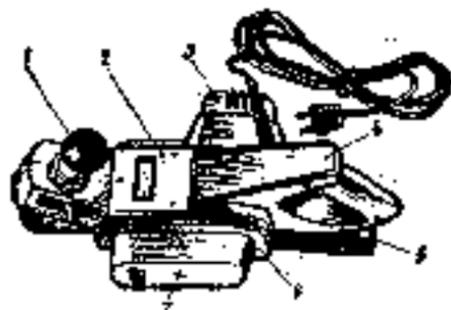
Рубанок электрический: 1 — рукоятка (ручка); 2 — крышка; 3 — электродвигатель; 4 — рубанок в открытом положении; 5 — передняя планка; 6 — корпус; 7 — резательная головка.
